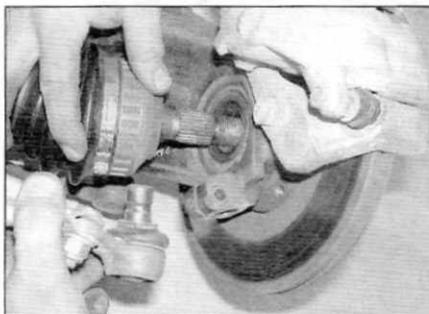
Оттяните поворотный кулак наружу и извлеките внешний шарнир полуоси из ступицы
